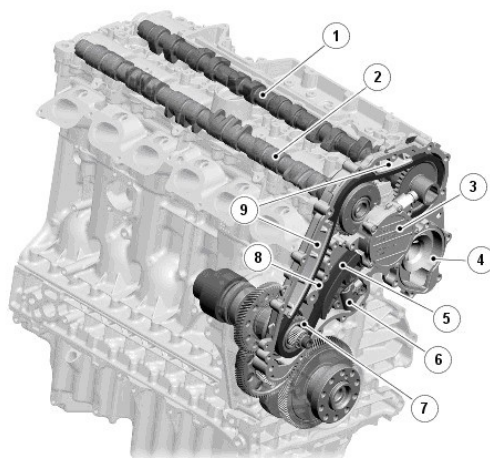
Элементы механизма регулировки фаз газораспределения бензинового двигателя 3.2L I6 Freelander 2
